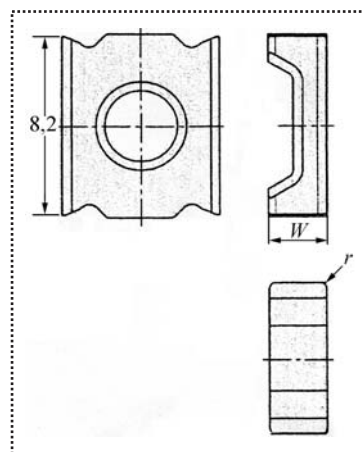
Режущая пластина фрезы MINITANG SLOT
